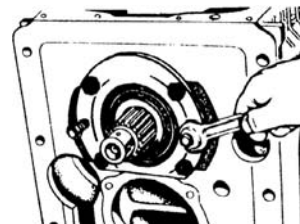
Спресовка стакана подшипника вторичного вала. Снятие вторичного вала, замена ведомой шестерни II ступени редуктора.
